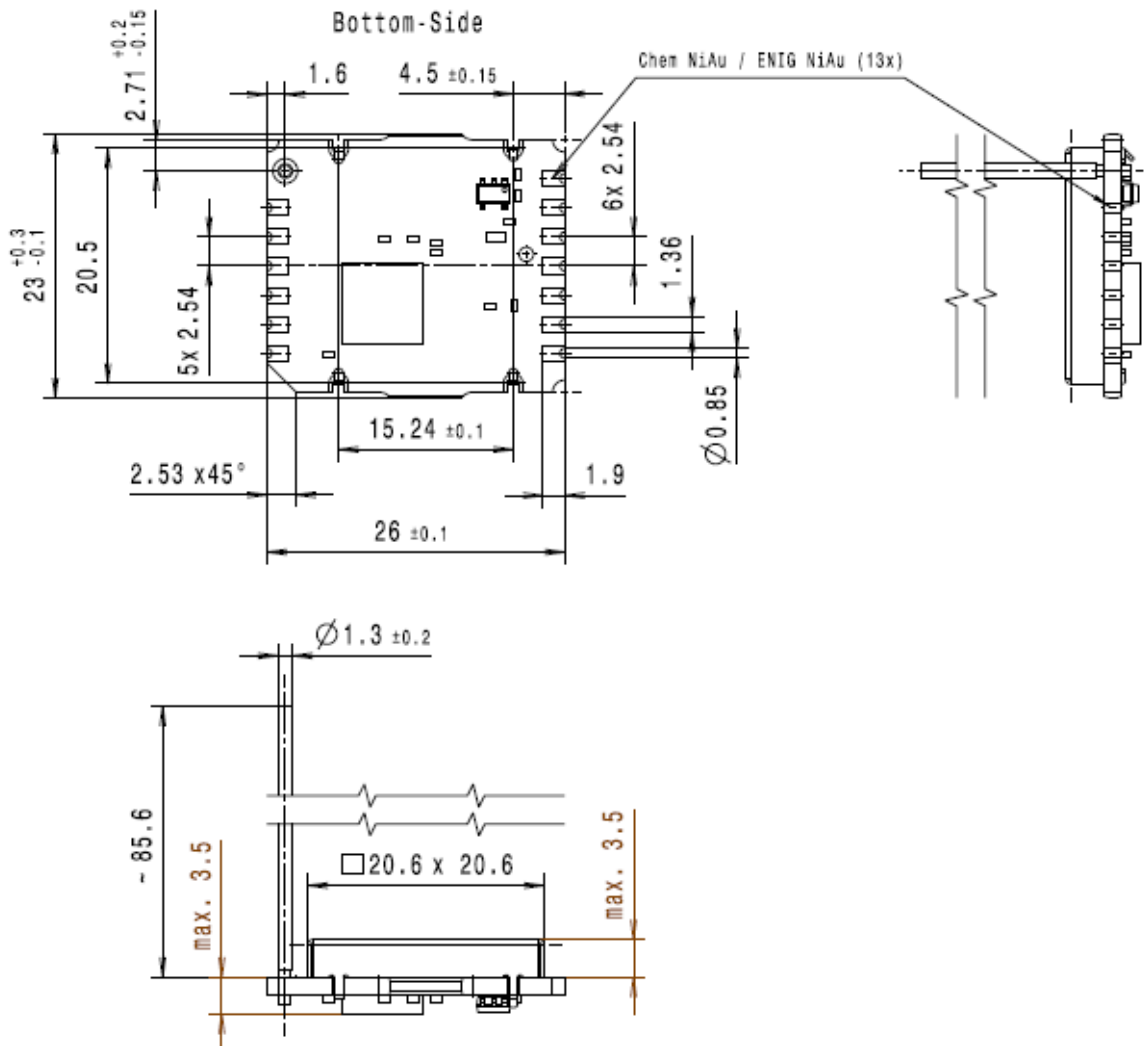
Abmessungen Funkempfangsmodul / Dimensions of RF stamp receiver
